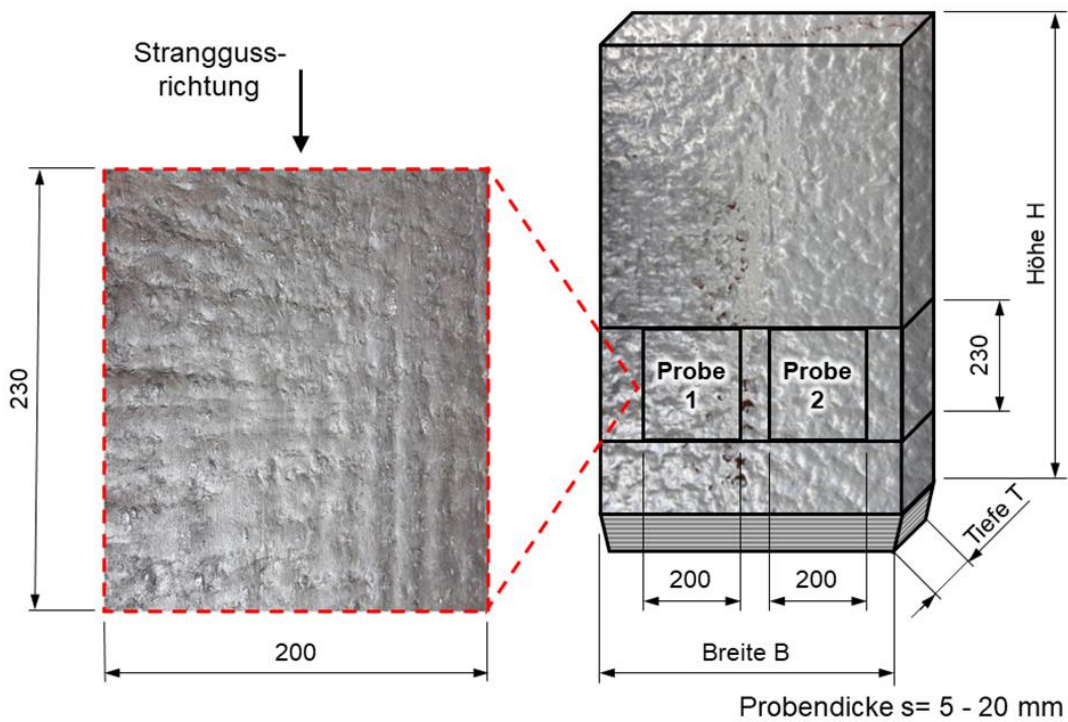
Prinzip der Probengewinnung aus Stranggussblöcken von Aluminiumlegierungen
